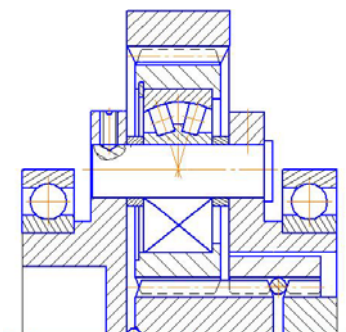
Передача типа 2К-Н с «плавающей» солнечной шестерней и двухопорными осями сателлитов
